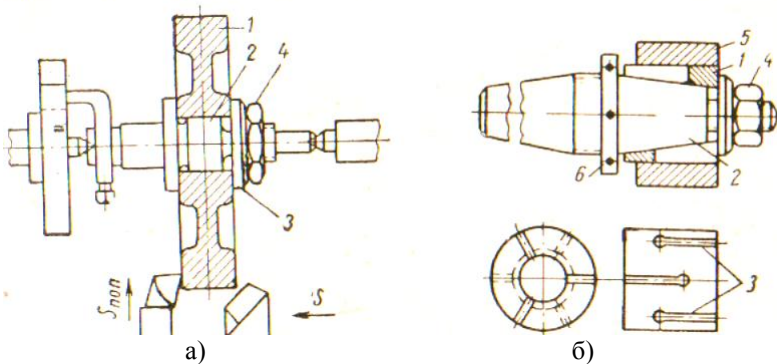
примеры использования оправок а) обработка диска на цельной цилиндрической оправке; б) обработка втулки на разжимной оправке
